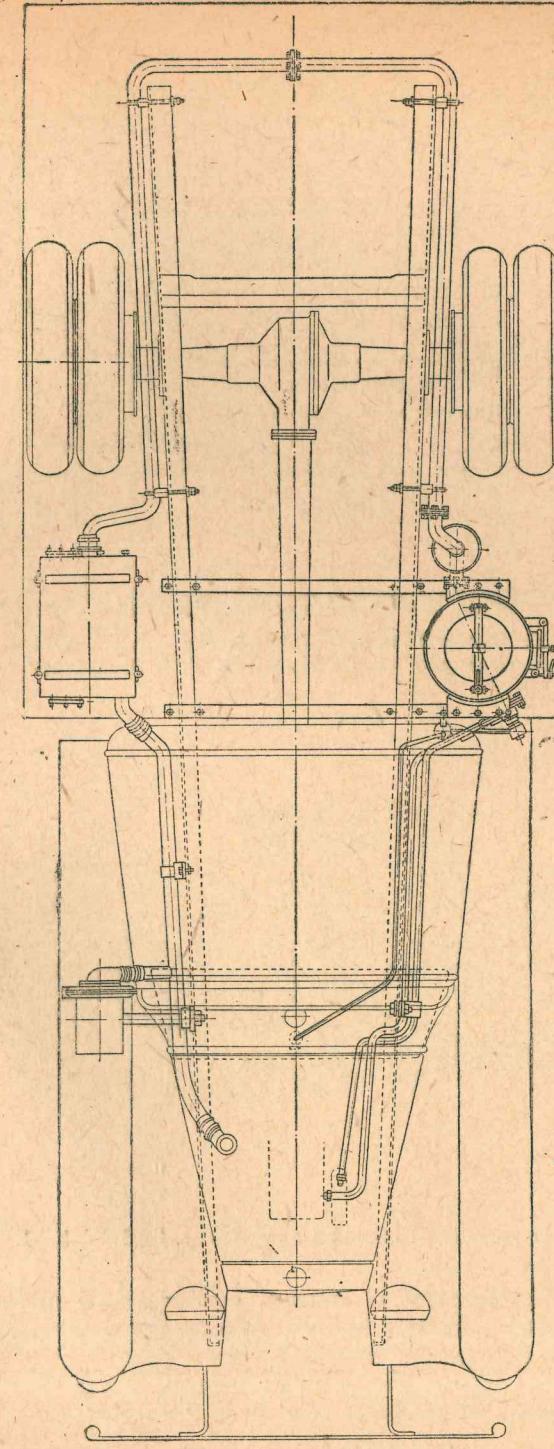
а. Автомобиль ГАЗ-АА, оборудованный древесноугольной установкой ЦНИИАТ-УГ-1, Вид сверху.
